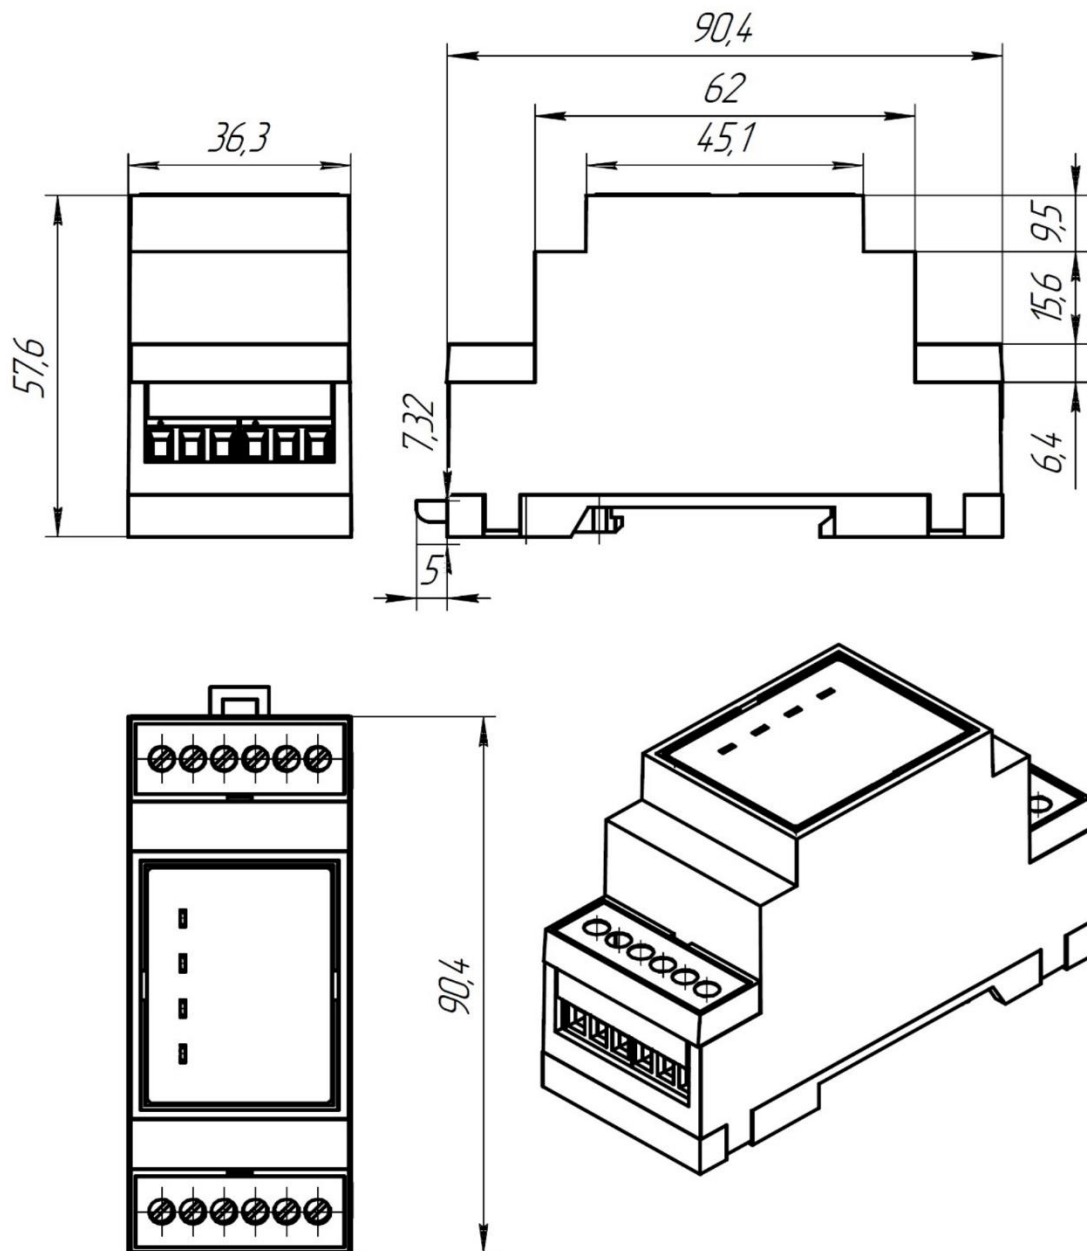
Габаритные размеры преобразователя Ethernet/RS-485/DCE332
